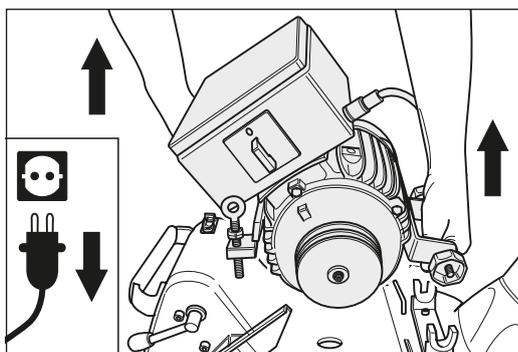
Desmontaje del motor de la carcasa de la máquina.
